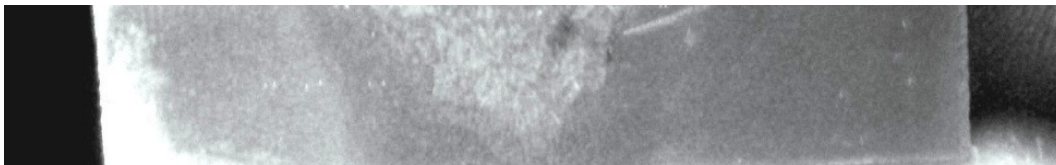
66 - Amostra do provete 6 (soldadura com vibração).
